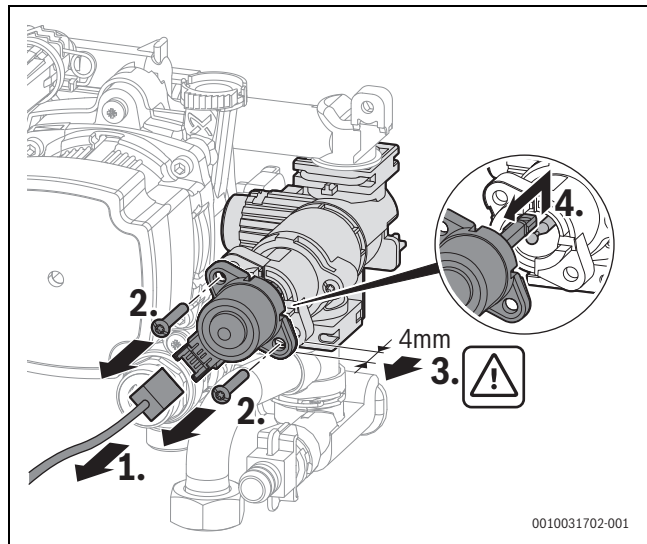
Desmontar el motor en la válvula de 3 vías (variante con tornillos)
